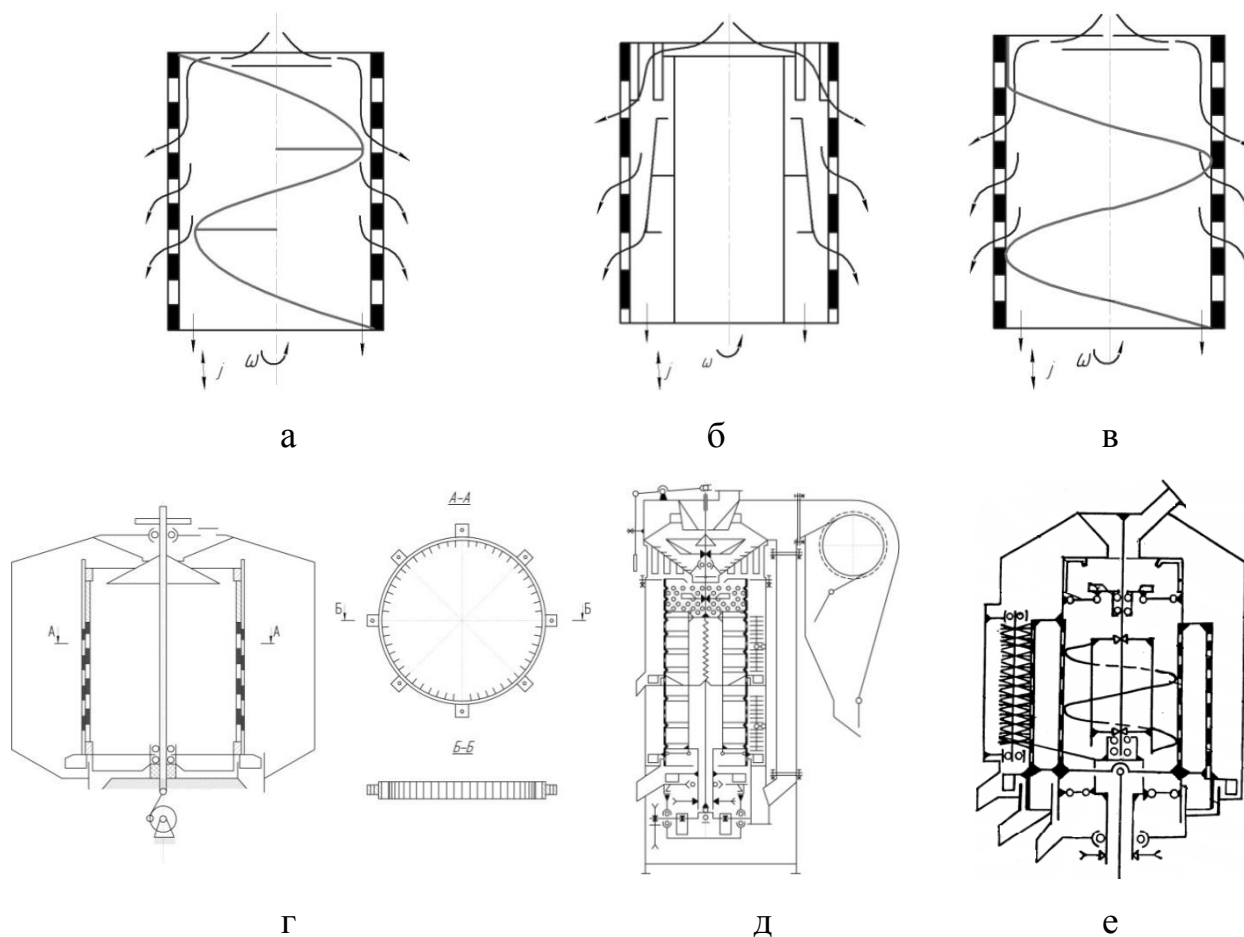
Устройства для стабилизации зернового материала в верхней части цилиндрического решета
